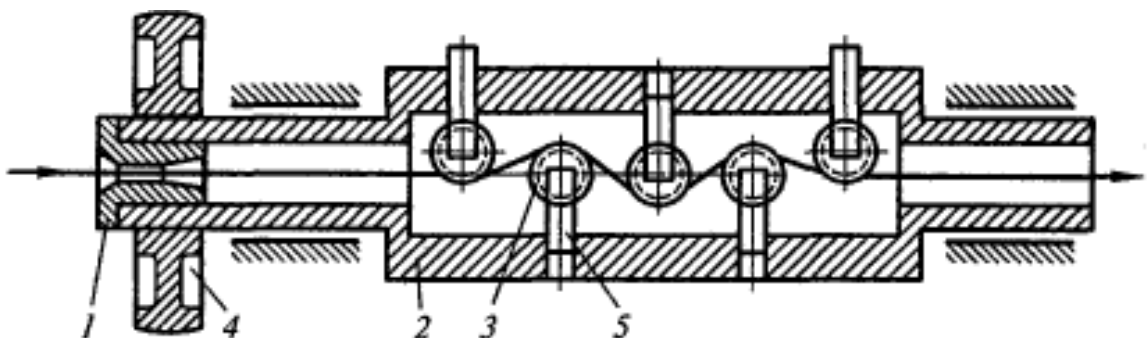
Схема верстату для правки дроту: 1 – калібруючи втулка; 2 – барабан; 3 – ролики; 4 – шків; 5 – державка ролика
